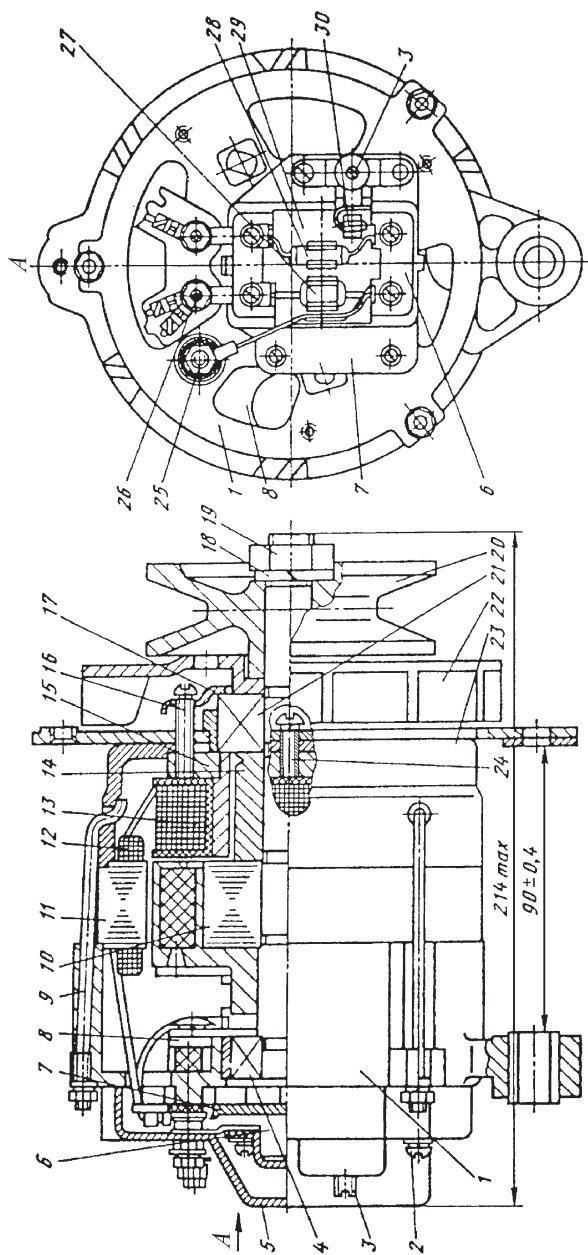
Тракторный индукторный генератор 46.3701:
